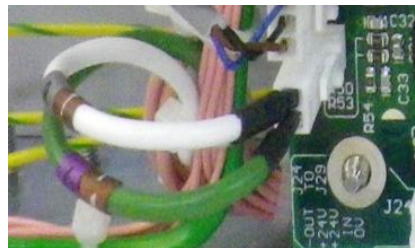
Cablu de compensație termocuplu la sistemul de comandă PCB
